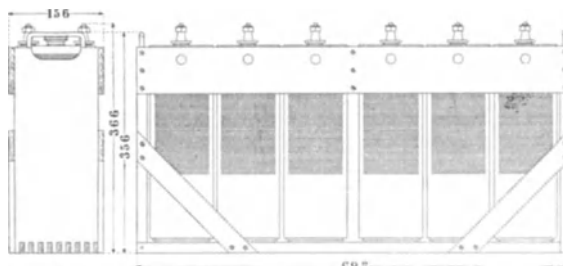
Maßskizze. 6 Zellen Type H 27, eingebaut in Holzträger.
